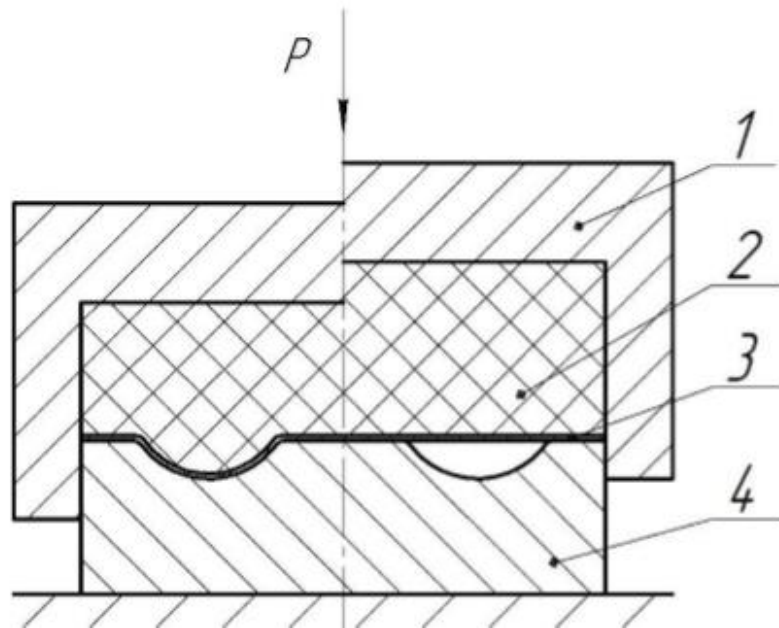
Схема кватістатичної витяжки поліуретаном у жорстку матрицю: 1 - контейнер; 2 - еластичний блок (поліуретан); 3 - листова заготовка; 4 – матриця
